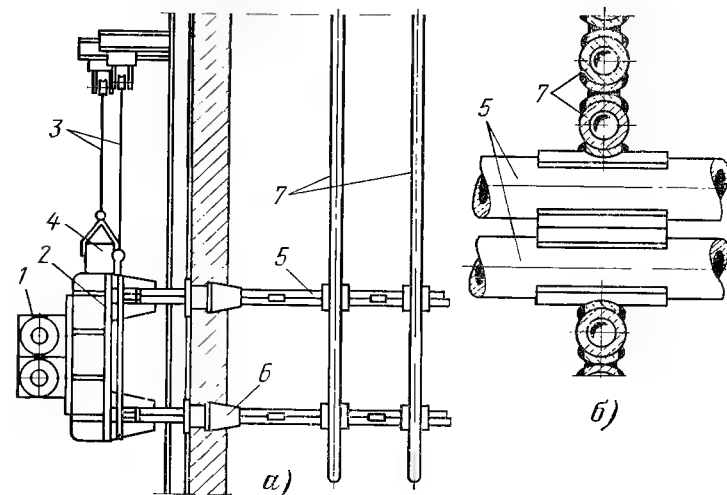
Вибрационное устройство для очистки вертикальных ширм. а — вид сбоку; б — узел сопряжения виброштанги с трубами; 1 — вибратор; 2 — плита; 3 — трос; 4 — противовес; 5 — виброштанга; 6 — уплотнение; 7 — труба ширмы.
